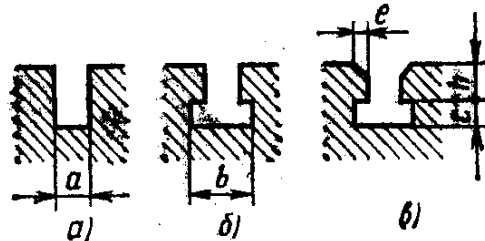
Способы фрезерования шпоночных пазов валов:
